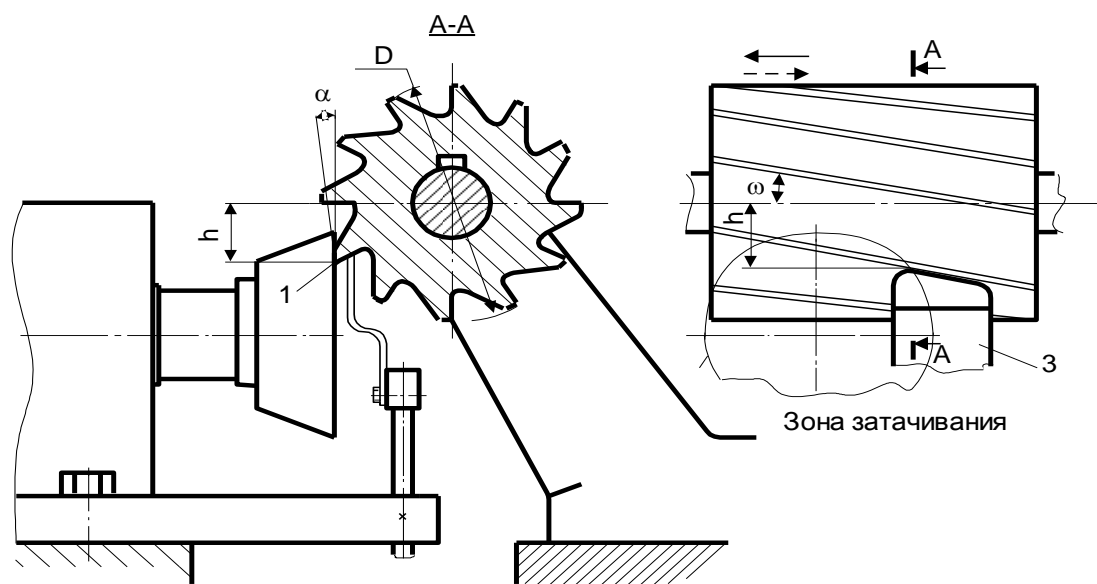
Схема установки фрезы при образовании главных задних поверхностей:
